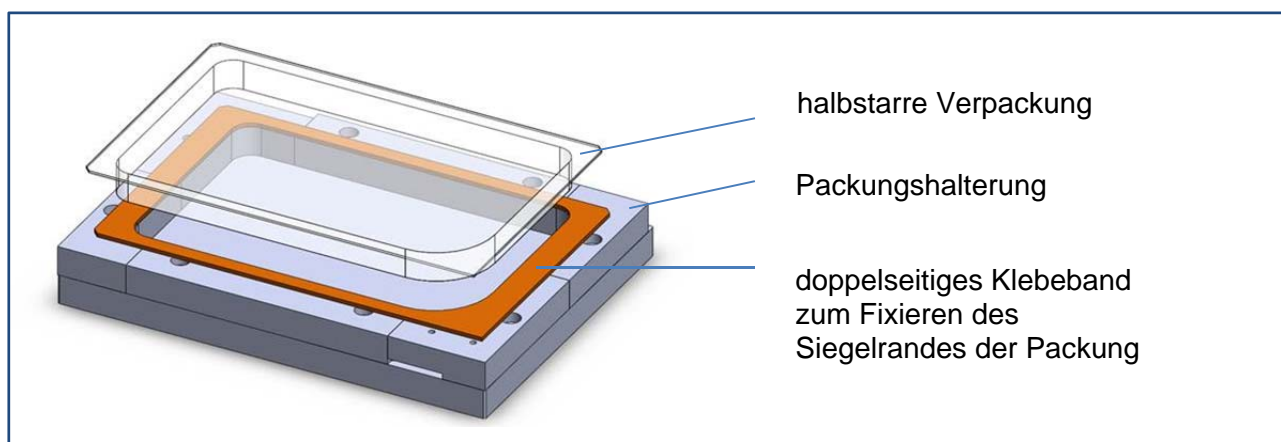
Beispielhafter Aufbau einer Packungshalterung für halbstarre Packmittel
